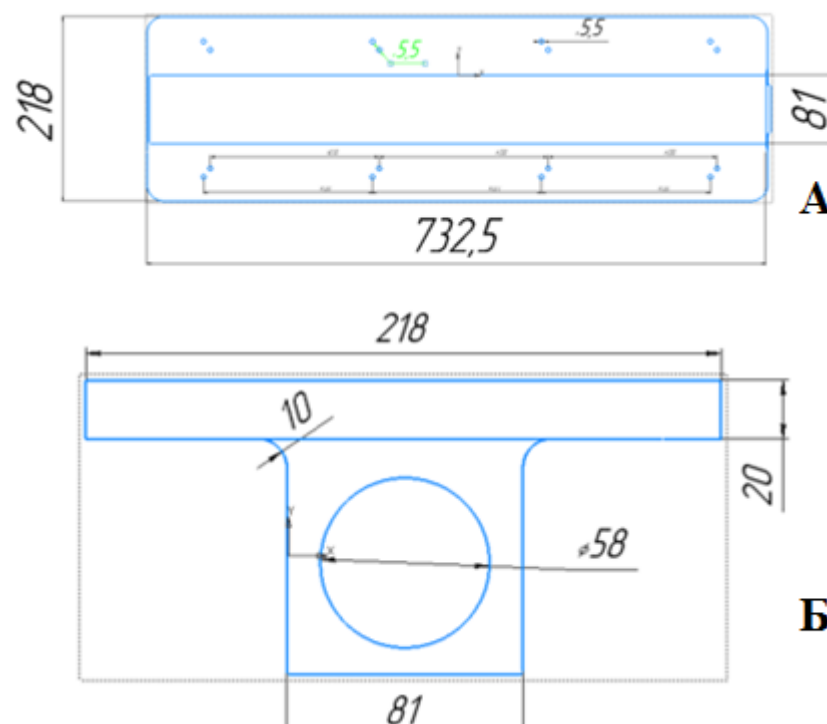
Схема чертежа корпуса светильника. А – вид снизу, Б – вид сбоку
